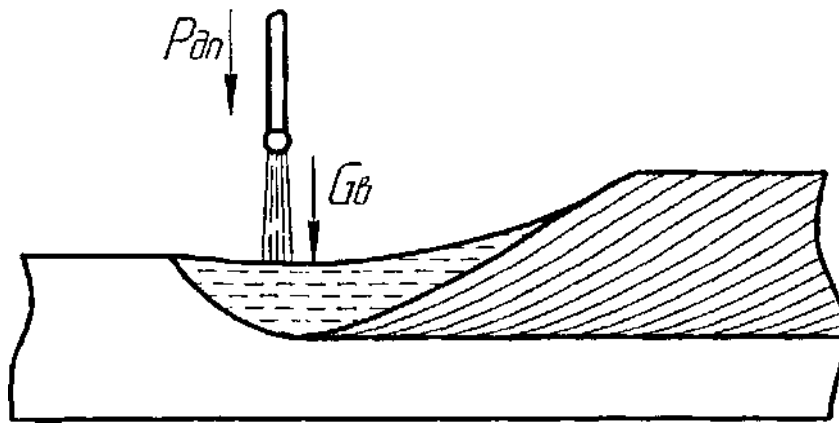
Сварочная ванна в момент паузы
